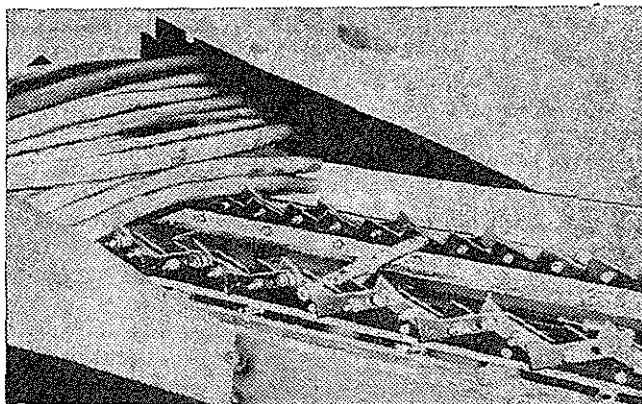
Сегментное бункерно-загрузочное устройство ЗУ-М для цилиндрических заготовок с прямолинейной и изогнутой осью.
